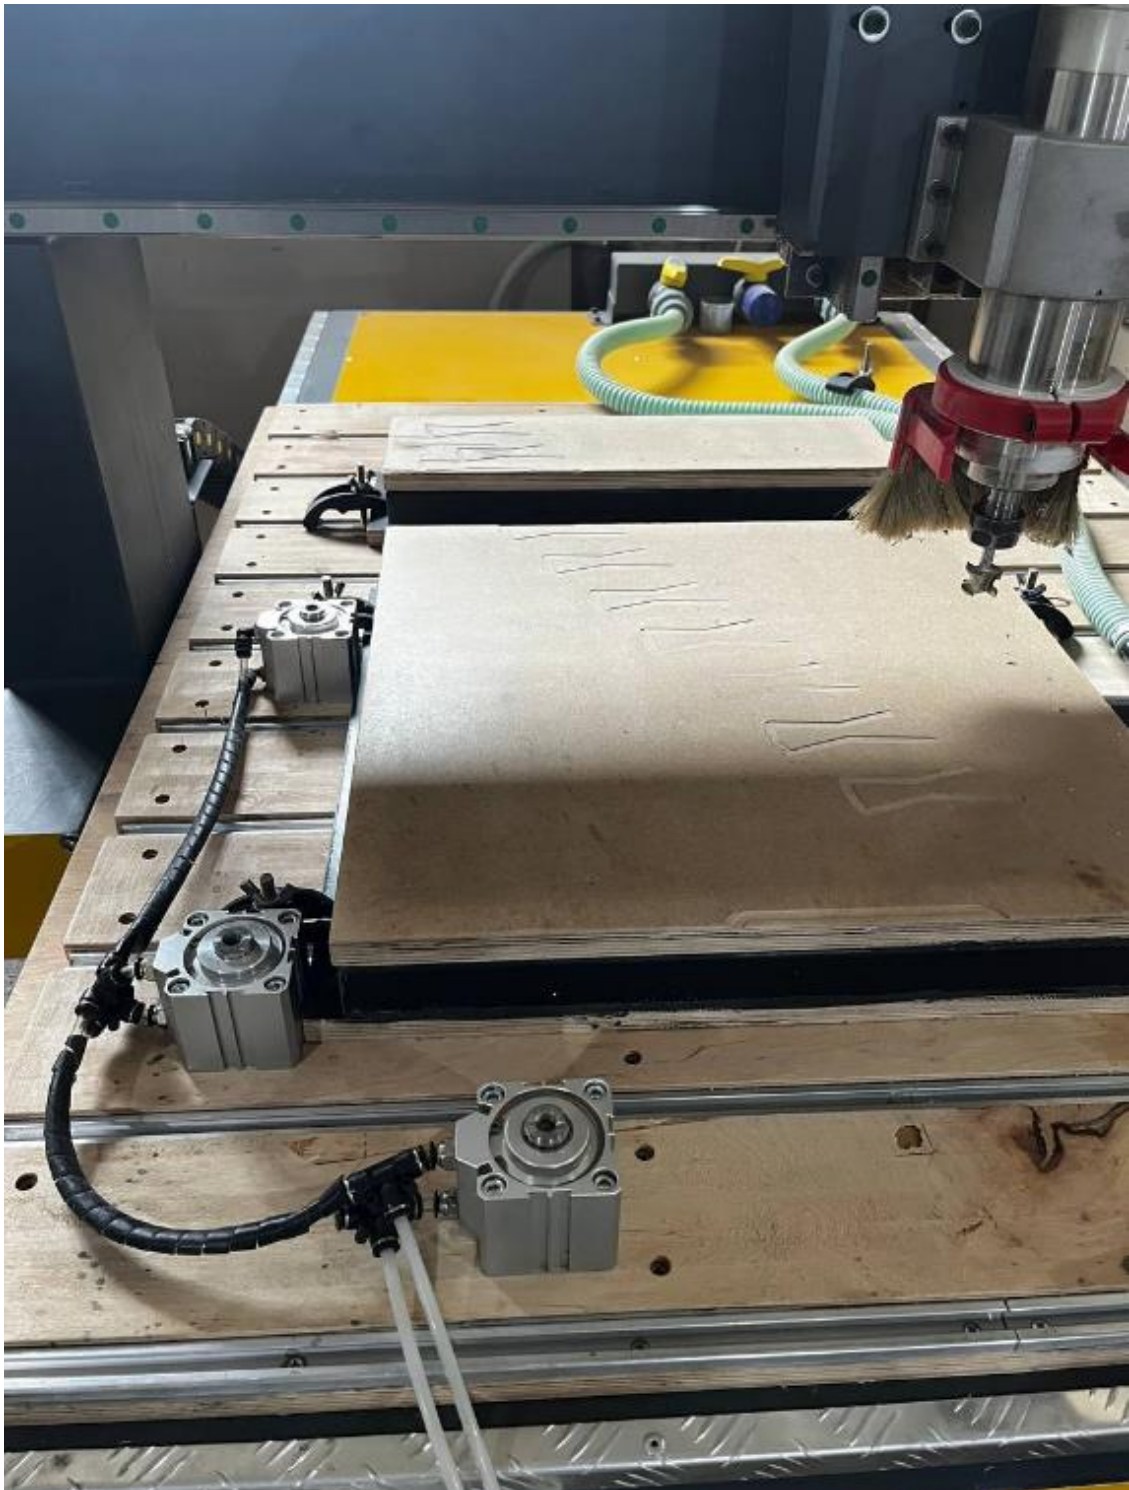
Конструкція комбінованого робочого столу верстата з елементами пневматичного базування
